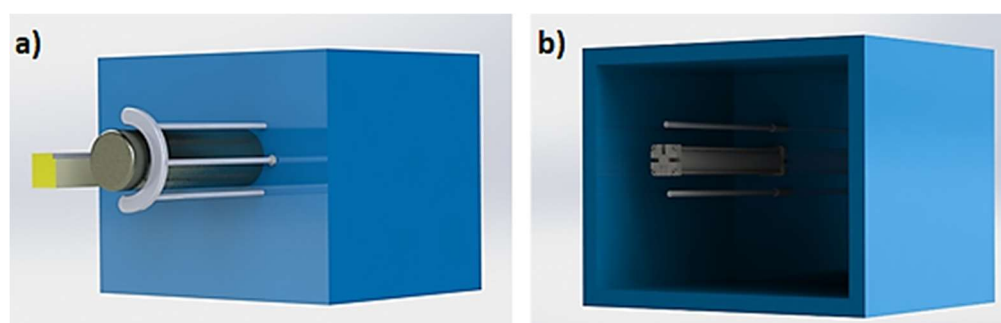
a) Vista frontal do extrator b) Vista traseira com cilindro pneumática e guias
